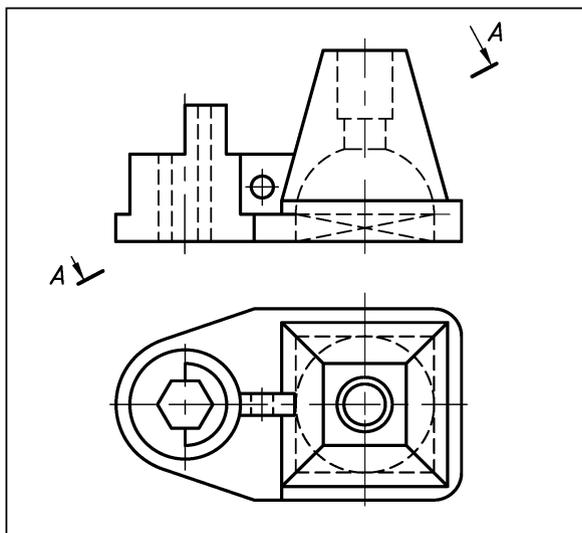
Вариант исходной заготовки чертежа детали с одной плоскостью симметрии для выполнения простых разрезов
